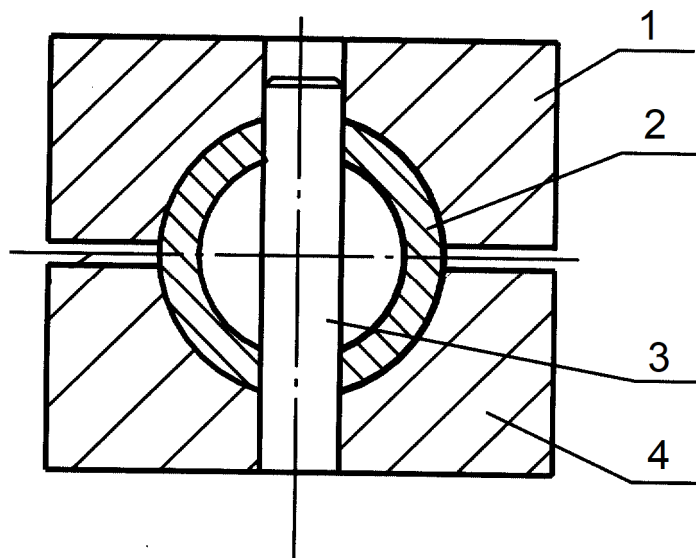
Схема операции: 1 – верхняя полуматрица, 2 – заготовка, 3 – цилиндрический упор, 4 – нижняя полуматрица
